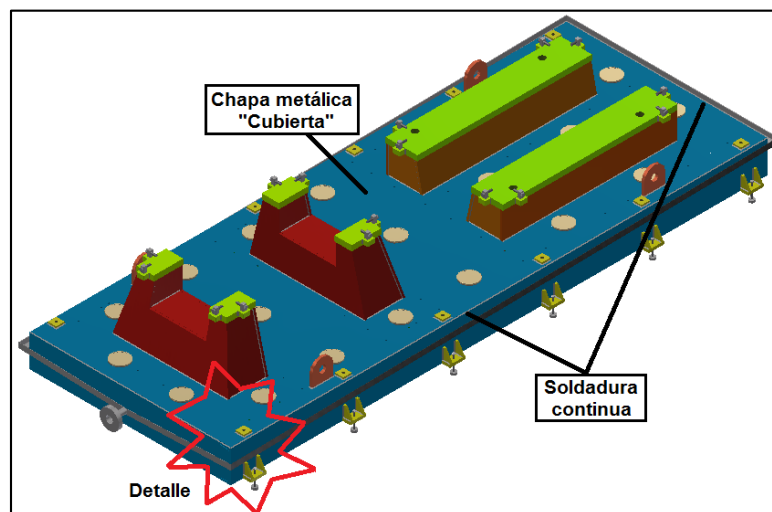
5 Chapa metálica soldada con las vigas UPN 300
